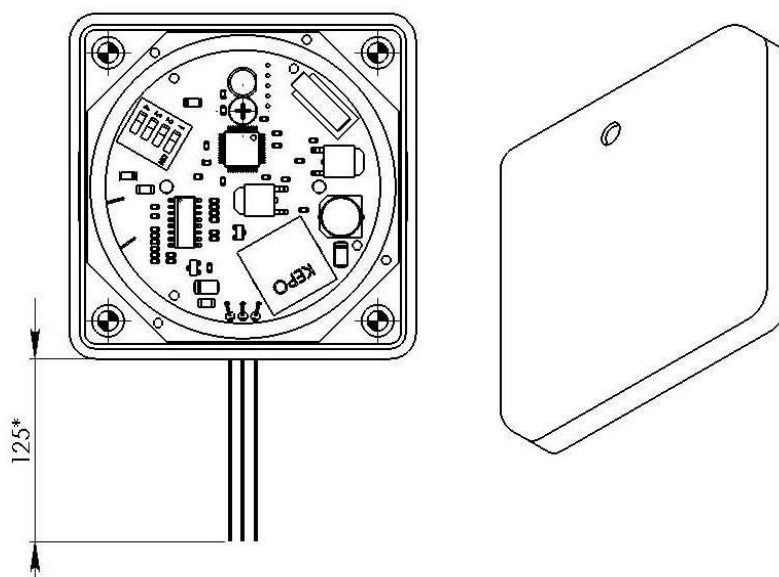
Внешний вид считывателя «Линд-ЕМ»
